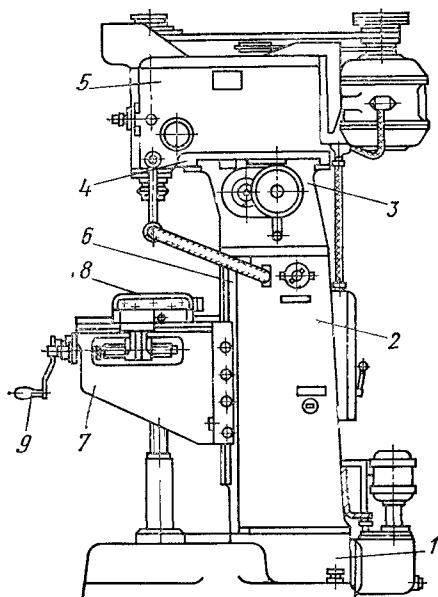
Вертикальный одношпиндельный шпоночно-фрезерный станок
